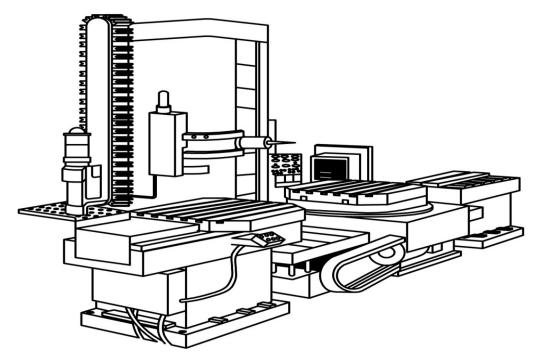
Обрабатывающий центр со вспомогательными столами
